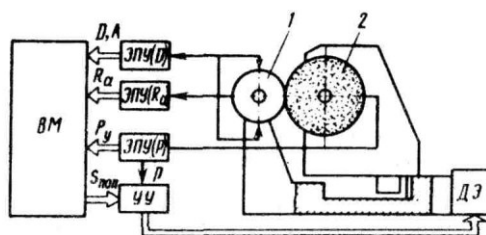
Система адаптивного управления качеством обрабатываемой детали при шлифовании: 1 — деталь; 2 — шлифовальный круг
